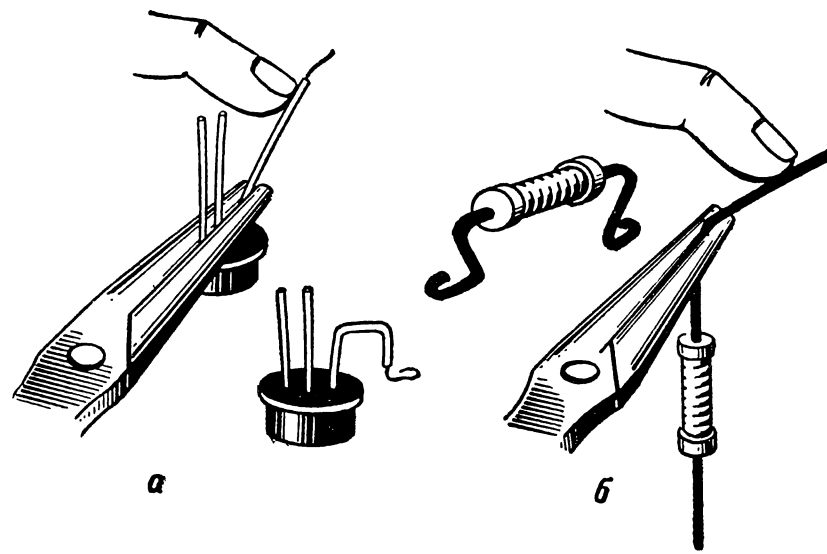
Подготовка деталей: а) транзисторов; б) резисторов
